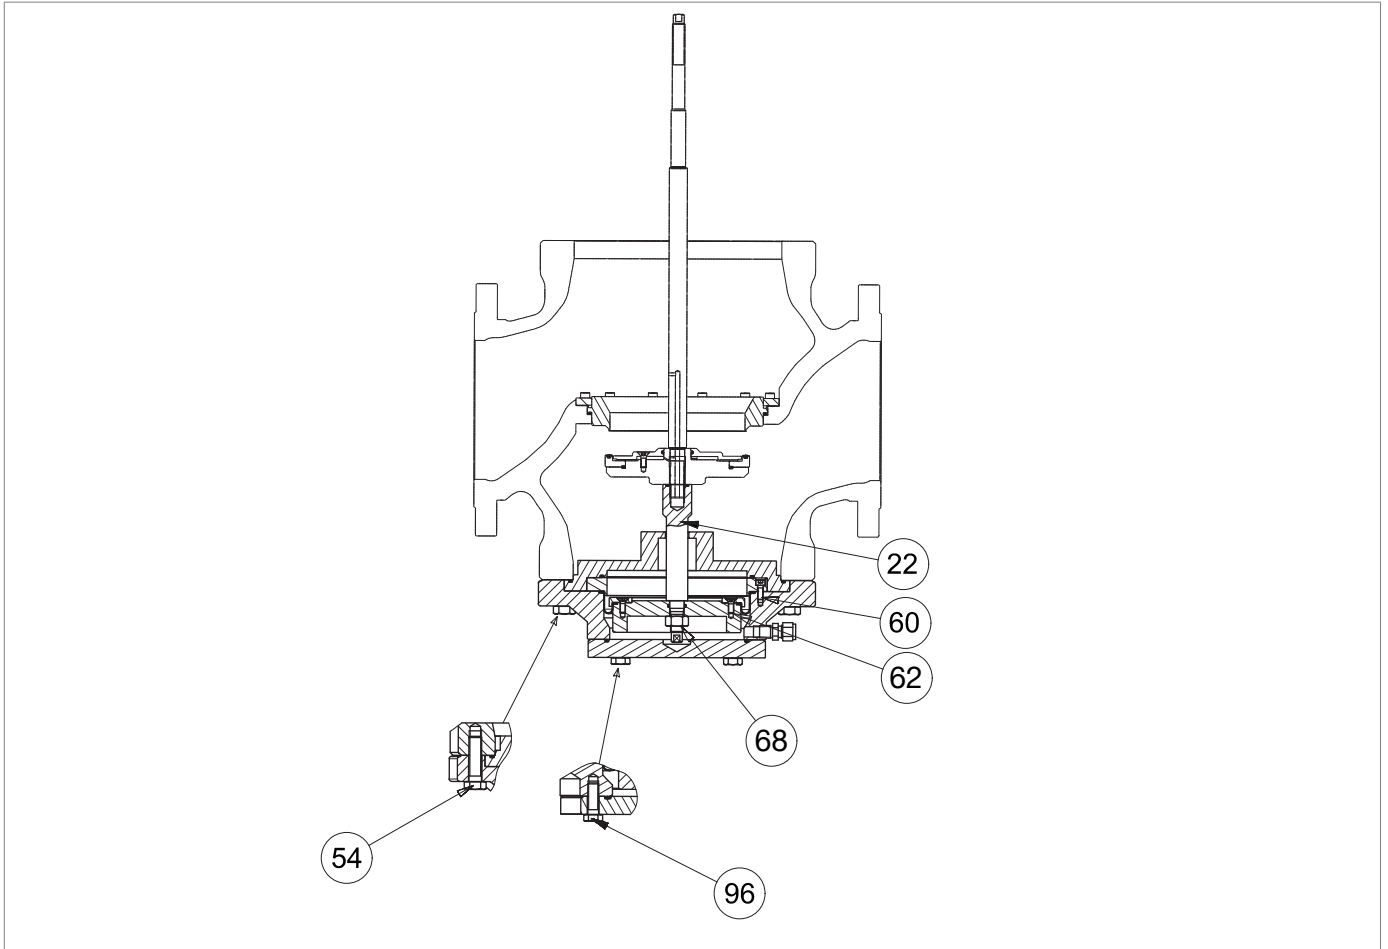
Couples de serrage moniteur intégré ER 6"-8"
